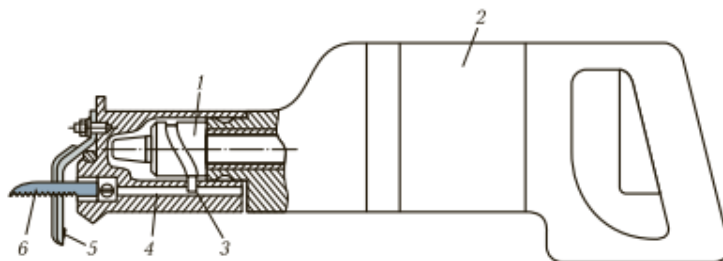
Механическая ножовка: 1 — барабан; 2 — корпус; 3 — палец; 4 — ползун; 5 — скоба; 6 — ножовочное полотно
